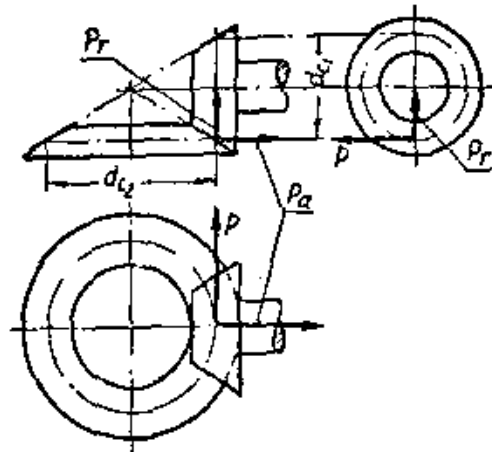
Схема усилий в зацеплении конических зубчатых колес
